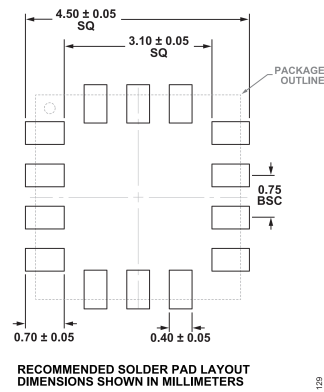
PCB フットプリント・パターンと寸法（単位：mm）
